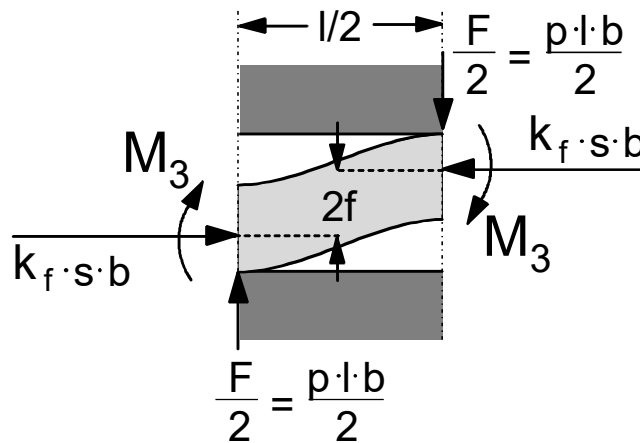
Momentengleichgewicht an einer Halbwelle nach /Siebel53/
